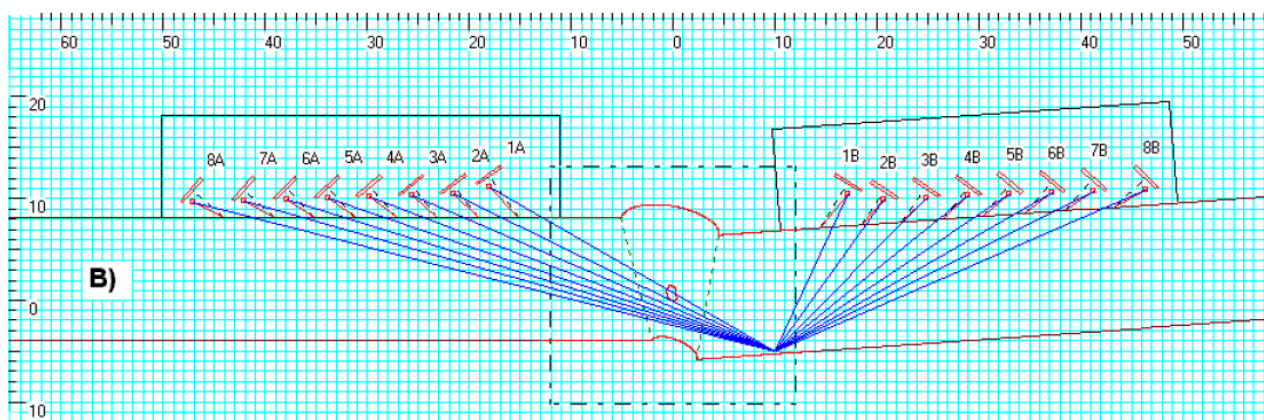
Контроль нижней области сварного соединения
